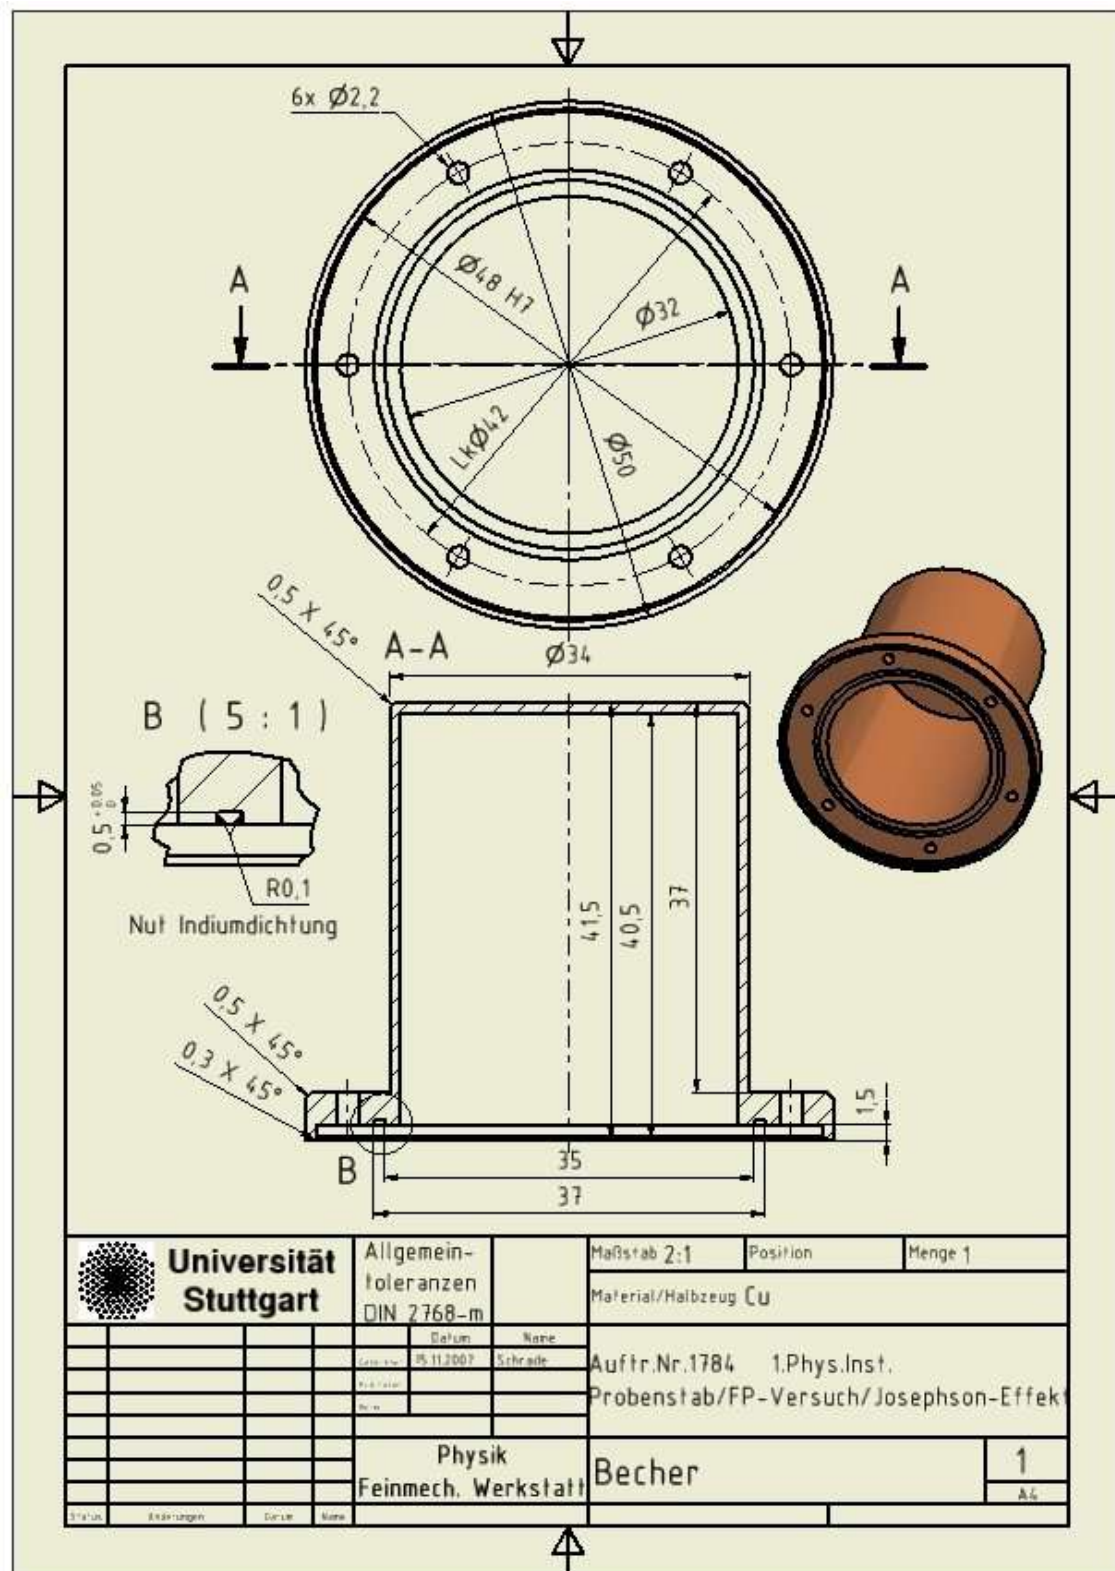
Technische Zeichnung für den Kupferzylinder.
